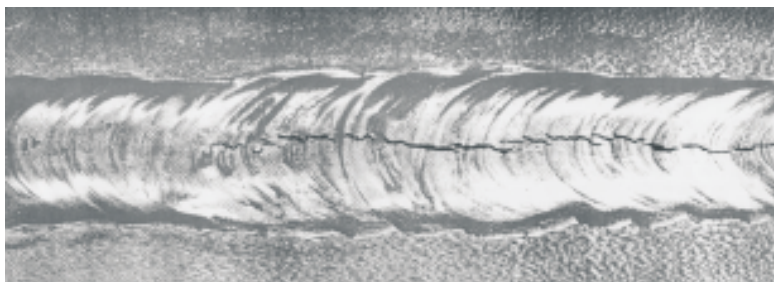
Горячие трещины в сварном шве алюминия
